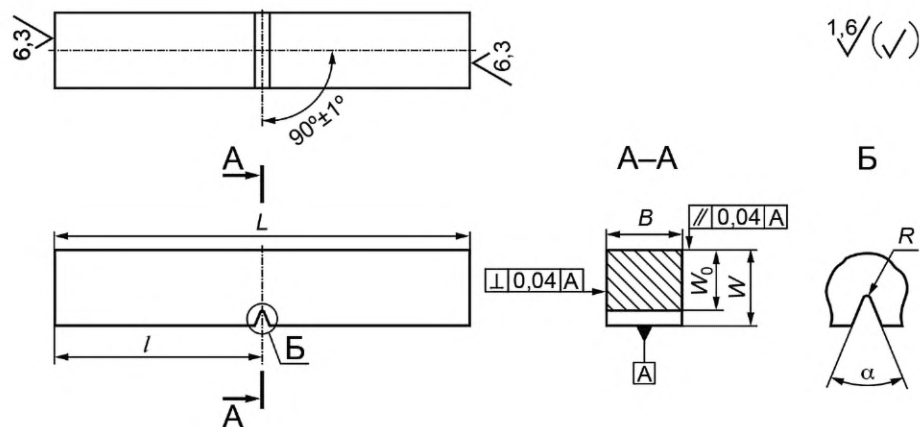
Эскиз стандартного и малоразмерного образцов Шарпи с V-образным надрезом
